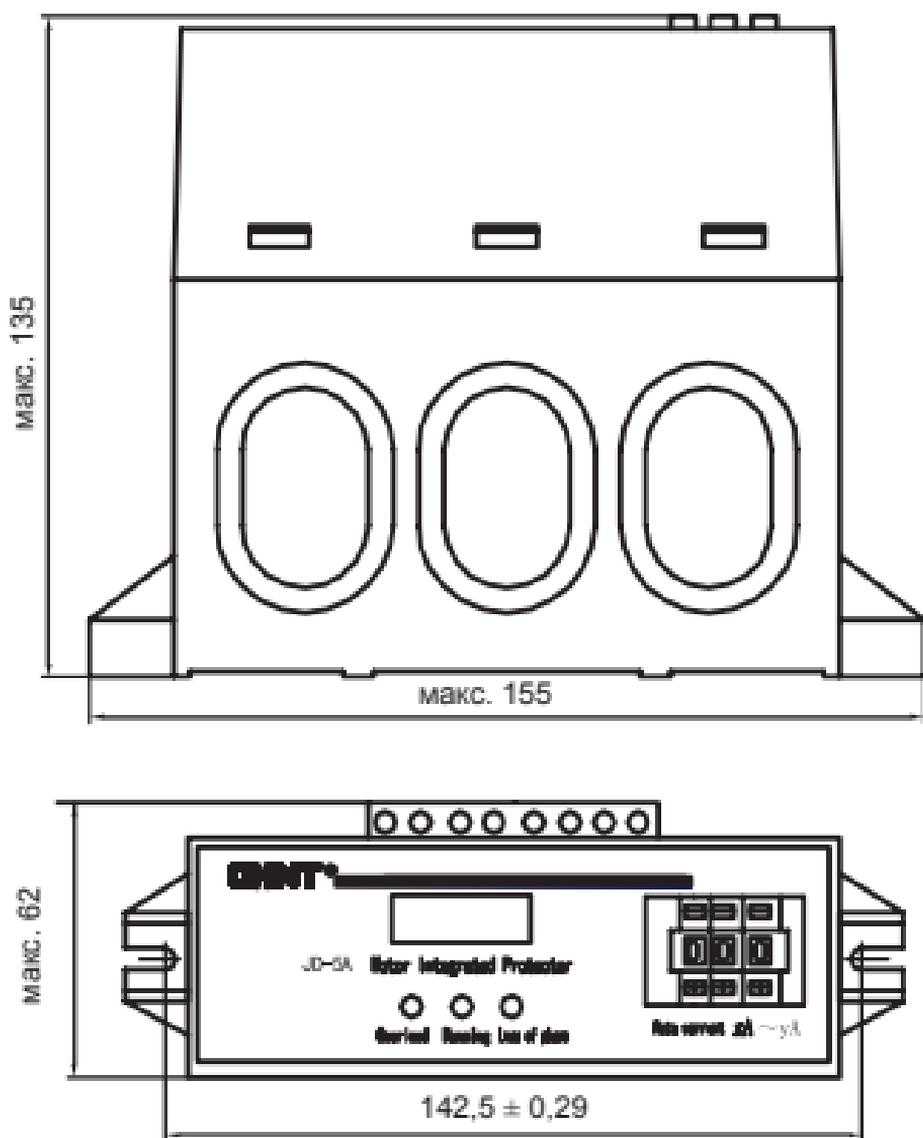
Габаритные и монтажные размеры для изделий с током нагрузки (80А ~ 400А)
